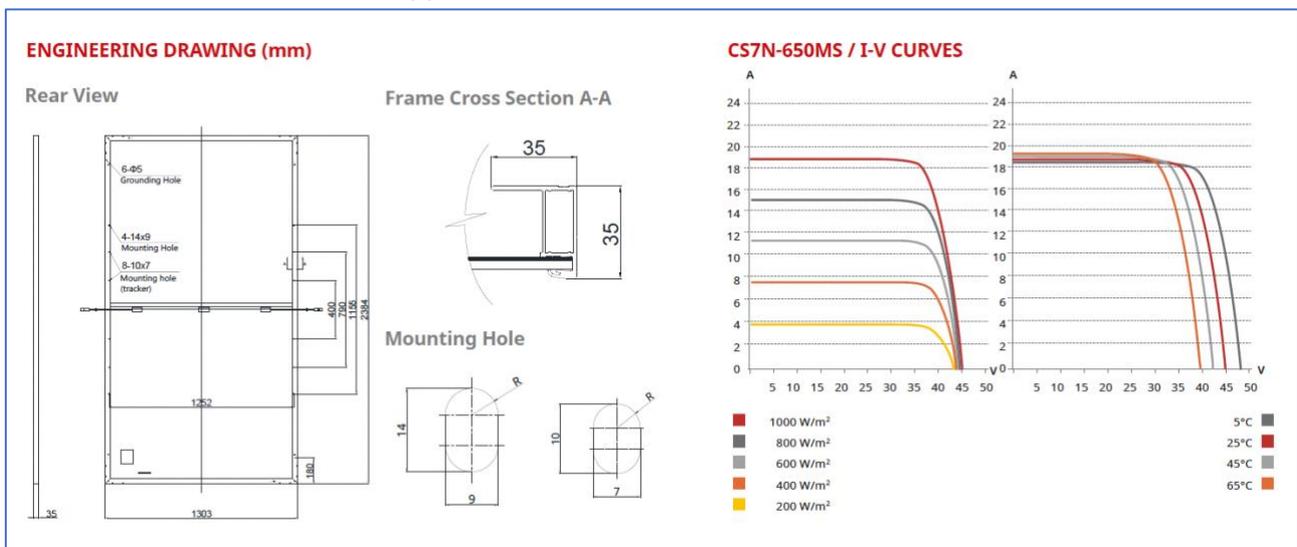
Vista posteriore pannello, particolare struttura supporto, curva I-V del modulo di progetto
